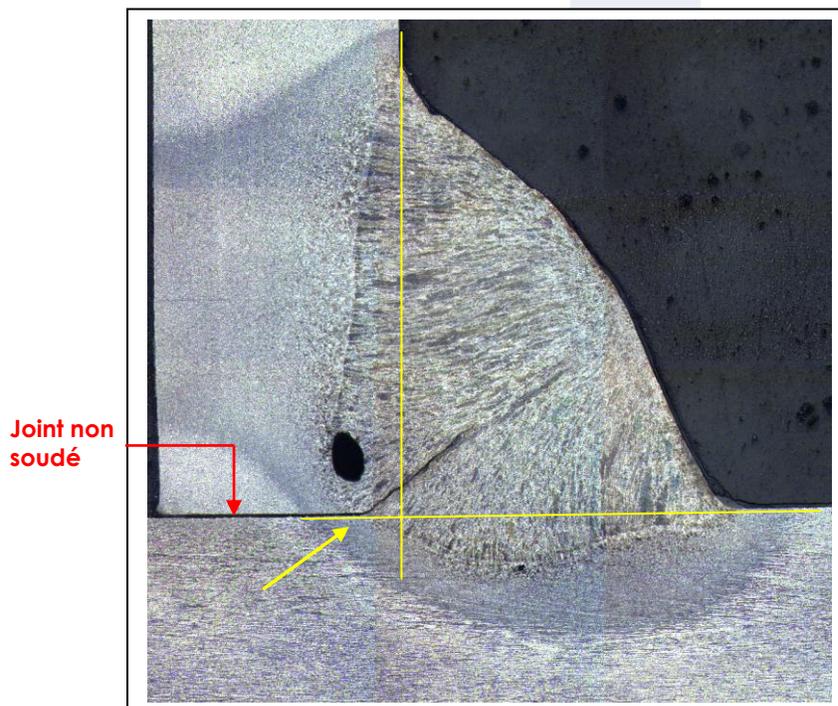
Fissure à la racine du cordon de soudure 2G1 - surface ext.
